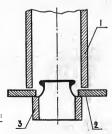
Запрессовка колпачка: 1 — трубка; 2 — шайба; 3 — колпачок,
